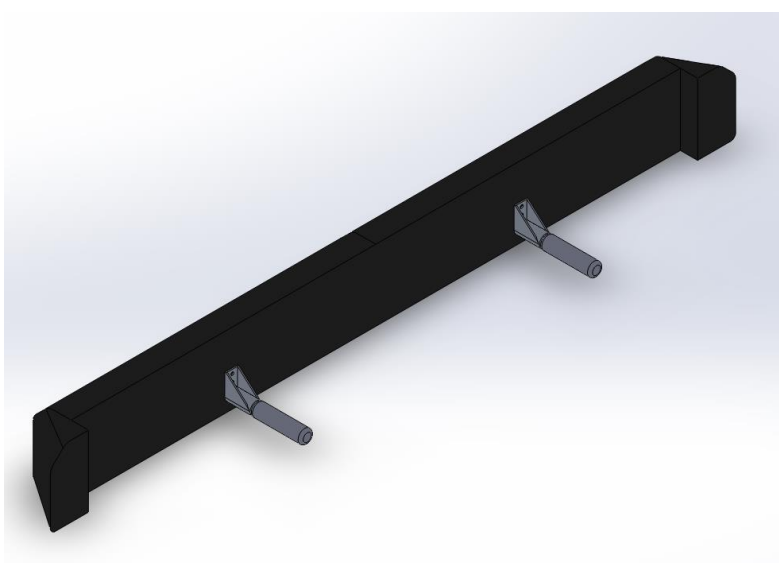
kit montaje carenado trasero + soportes. Fuente: propia.
